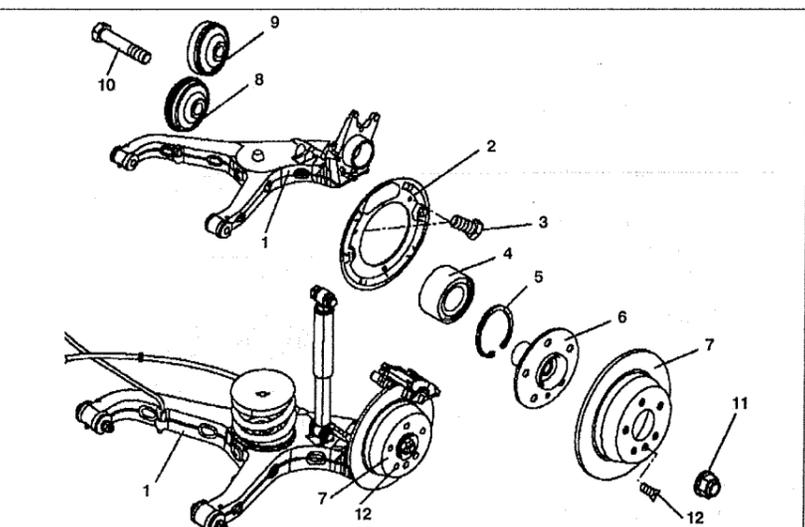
Снятие и установка задней подвески: 1. Нижний рычаг, 2. Защитный щиток тормозного механизма, 3, 10. Болт, 4. Подшипник, 5. Стопорное кольцо, 6. Ступица колеса, 7. Тормозной диск, 8. Нагнетающее устройство с ротором для ABS, 9. Нагнетающее устройство без ротора, 11. Гайка M22, 12. Болт M8x16.
